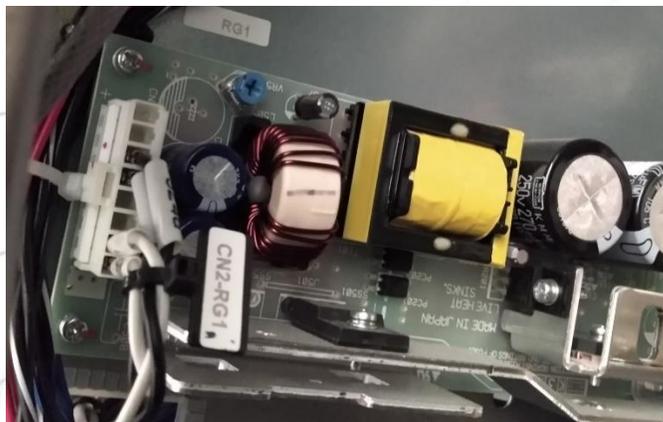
RG1 en panel lateral detrás de la unidad PCB.
